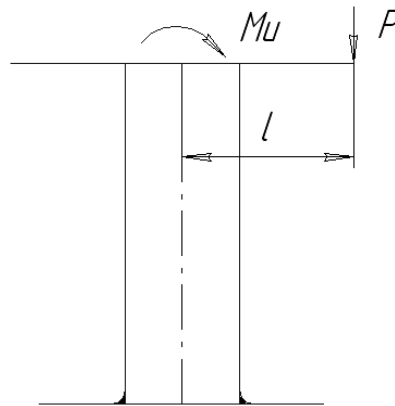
Схема для розрахунку зварювального з'єднання
